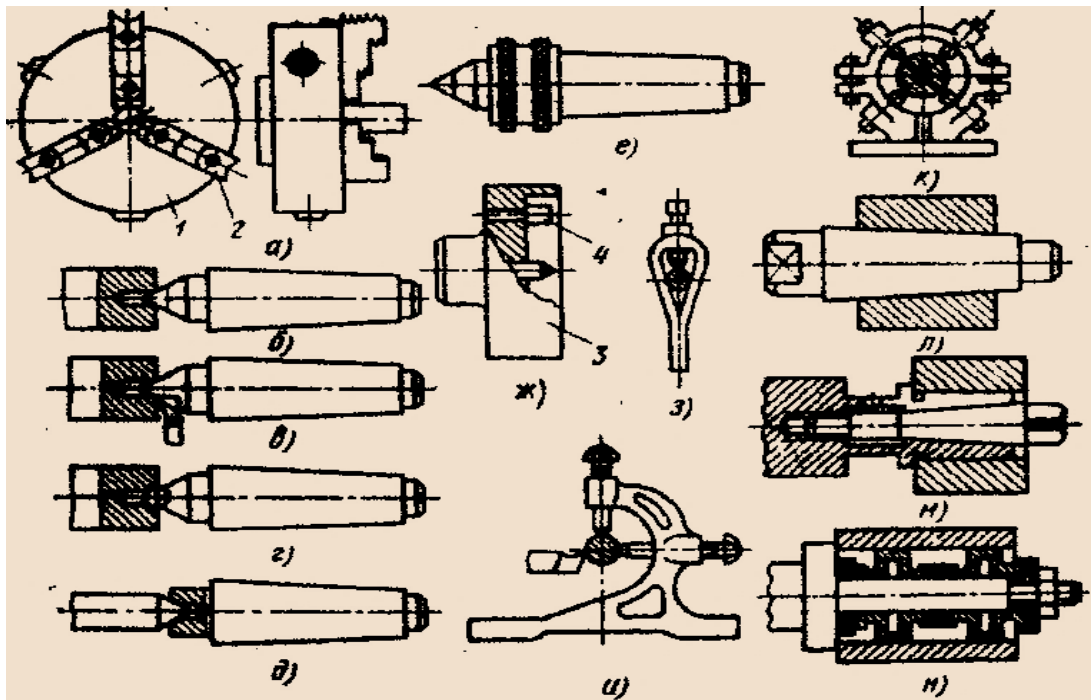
Приспособления для закрепления заготовок на токарных станках:
